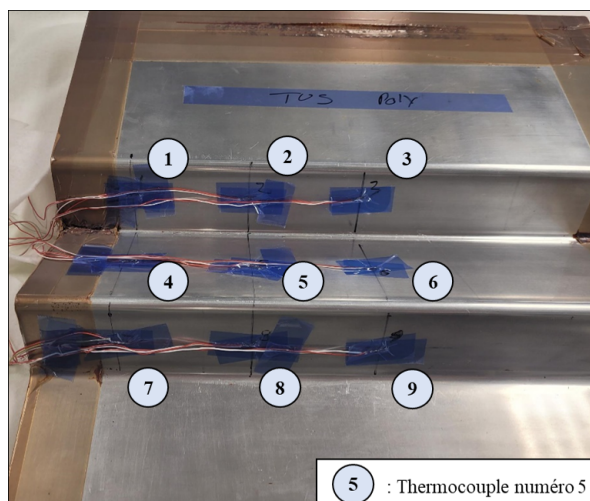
Position des 9 thermocouples sur l'outillage en aluminium.
